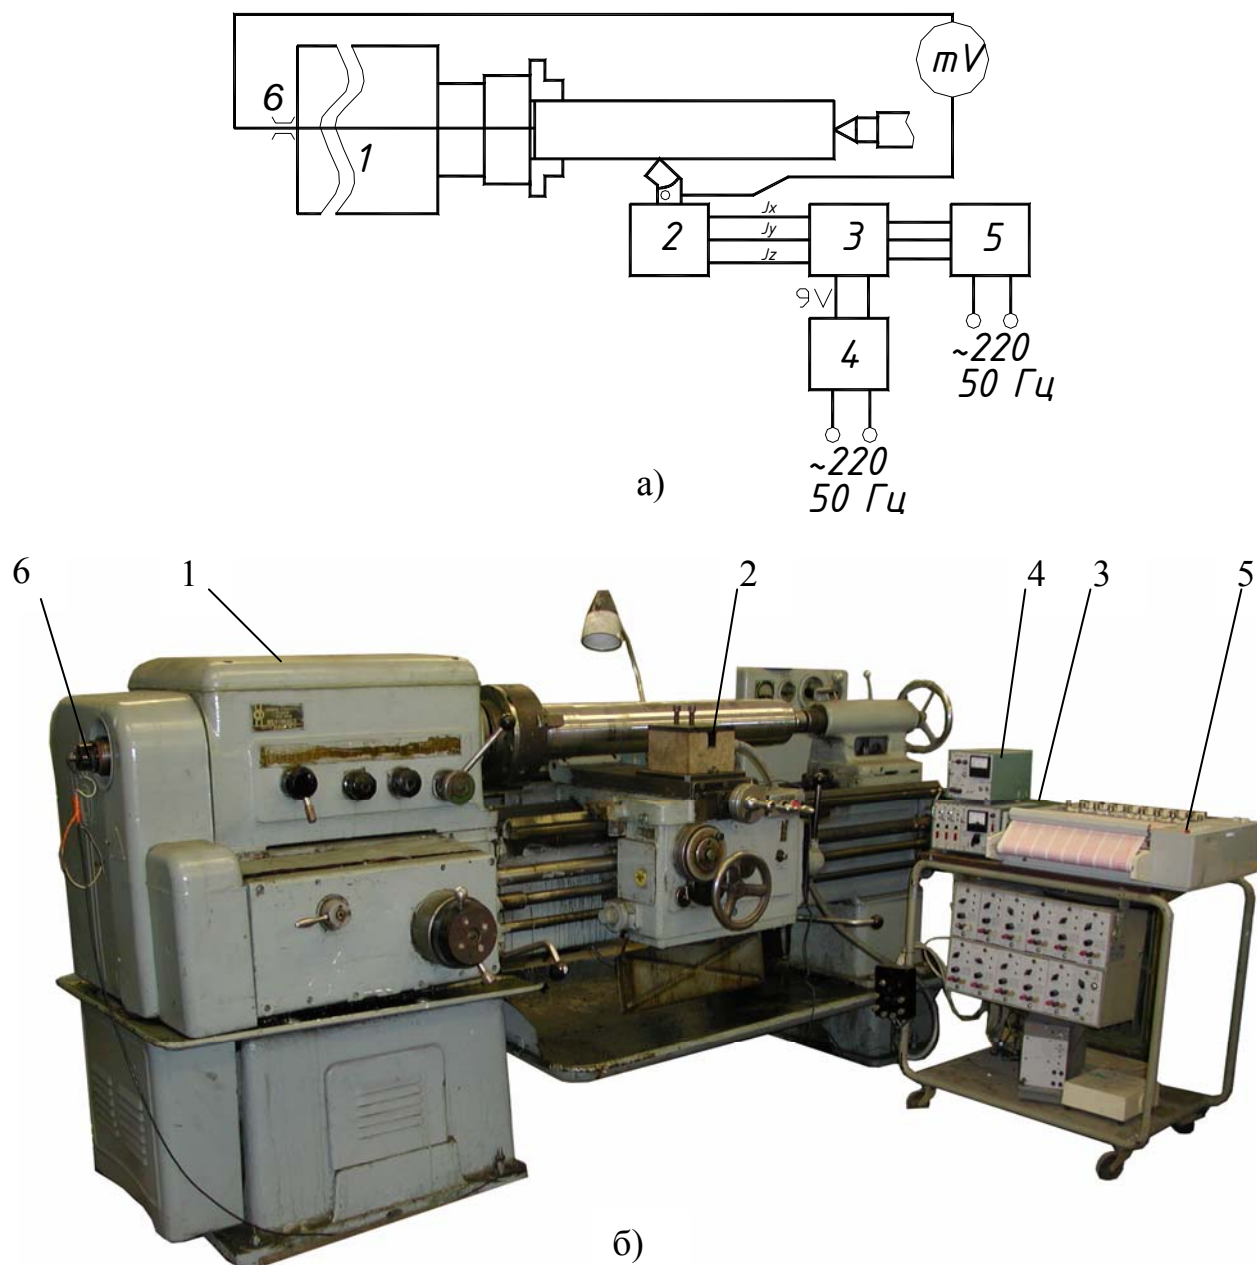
Экспериментальная установка: а) электрическая схема, б) внешний вид (1-токарно-винторезный станок 1К62; 2- трехкомпонентный тензоэлектрический динамометр; 3 - тензоусилитель «Топаз-4-01»; 4 –блок питания; 5 - самопишущий прибор НЗ38-8П; 6 –вращающийся токосъемник).
